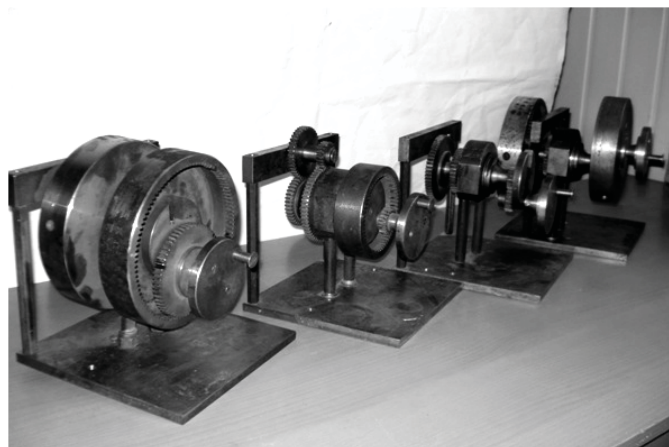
Внешний вид моделей механизмов, по схемам 1, 2, 3, 4 слева направо и схема
